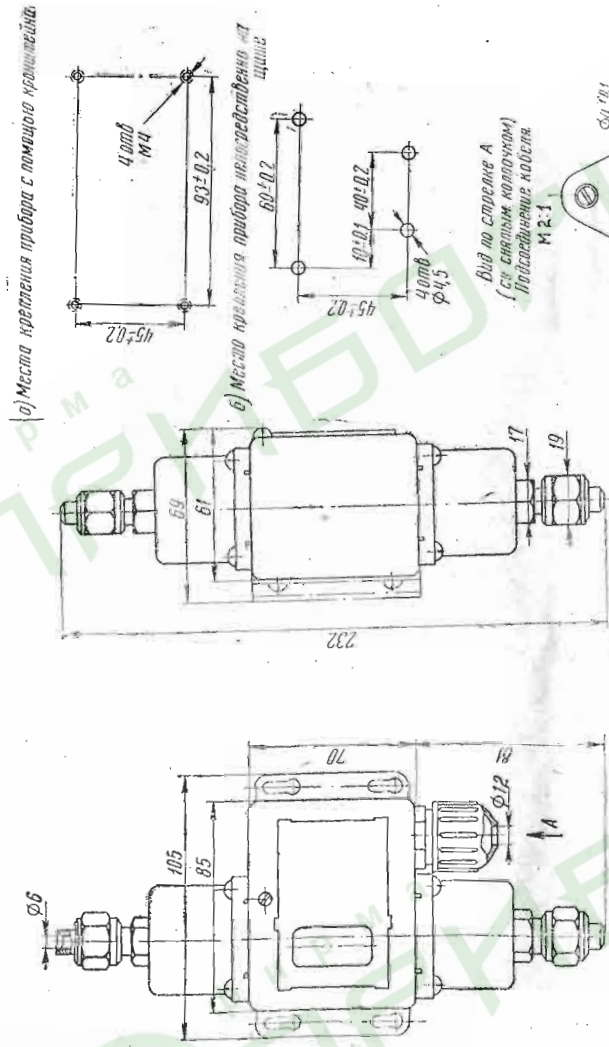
Габаритные и присоединительные размеры прибора РКС-1. Прибор крепится: а) с помощью кронштейна (дет. 107-00-22); б) непосредственно на щите.
